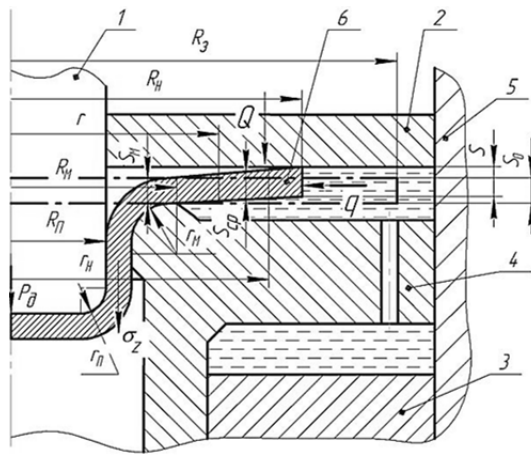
Розрахункова схема витягування з підпором фланця заготовки для аналізу інженерним методом:
